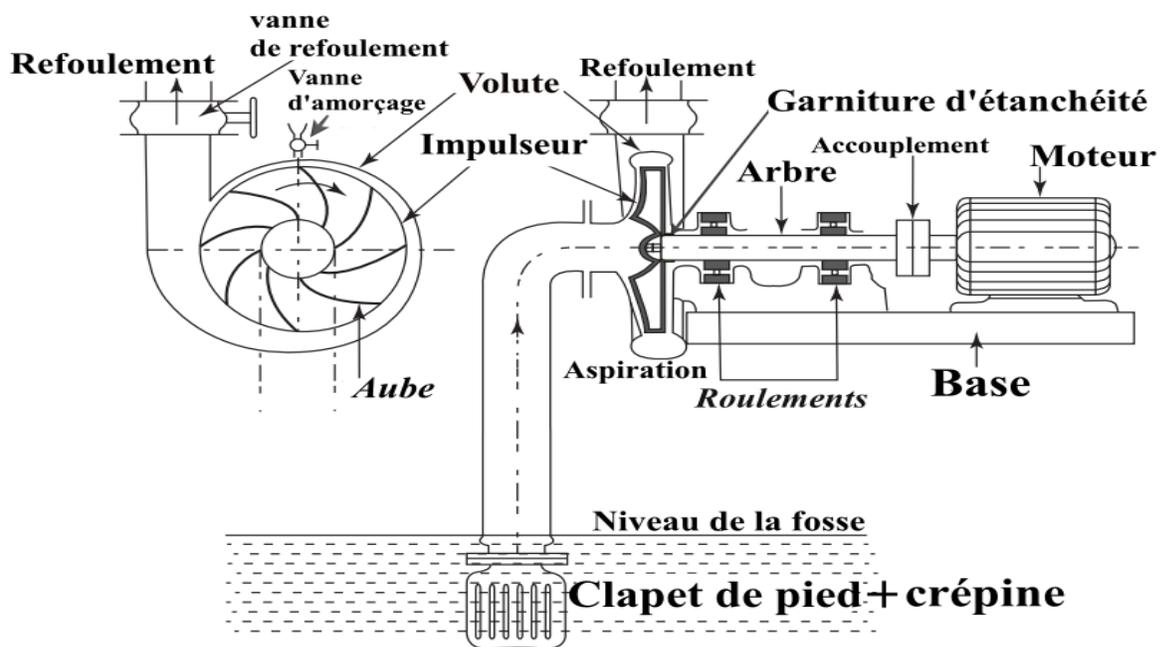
Schéma d'une installation de pompe centrifuge. [7]
